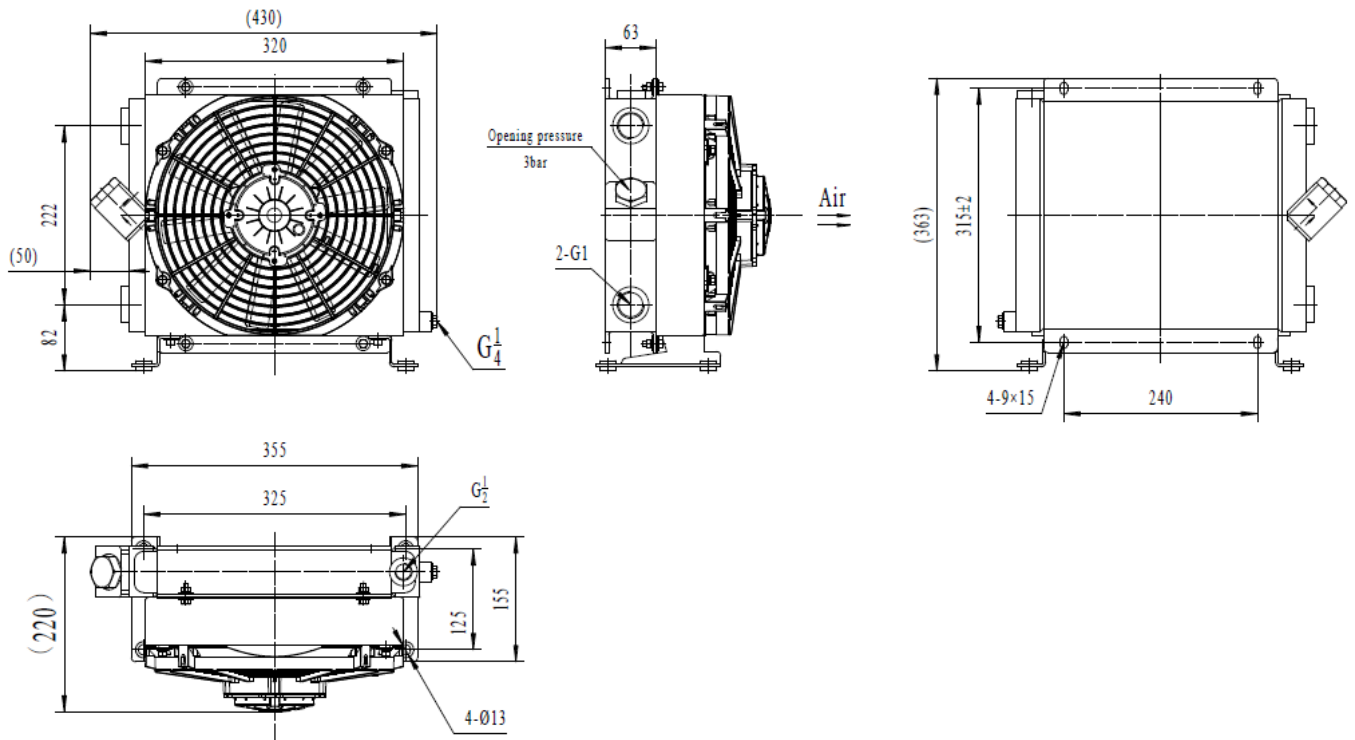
Габаритные и присоединительные размеры АН-Т11-В-12DC
